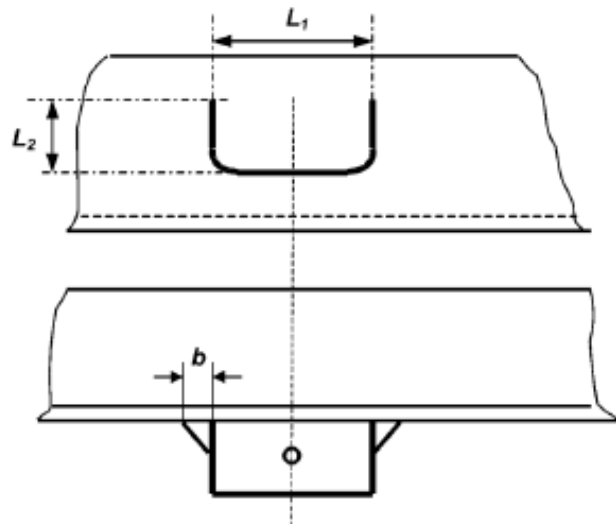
Esquema soldadura soportes fijación. UNE-EN 12252
